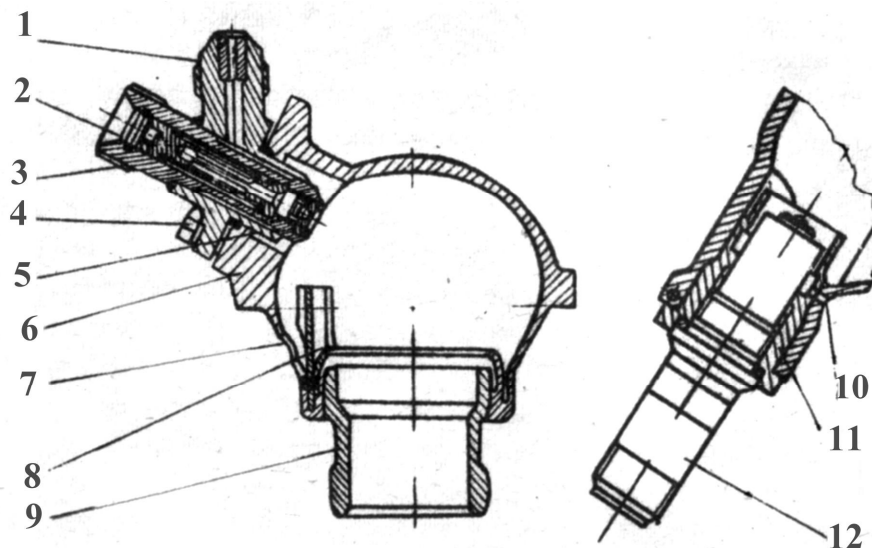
Пусковой воспламенитель: 1 – кислородный штуцер с жиклером; 2 – фильтр топливный; 3 – форсунка пусковая; 4 – болт крепления форсунки; 5 – распылитель; 6 – корпус; 7 – отверстие подвода воздуха; 8 – экран-дефлектор; 9 – сопло воспламенителя; 10 – отверстие для обдува; 11 – втулка; 12 – свеча зажигания
